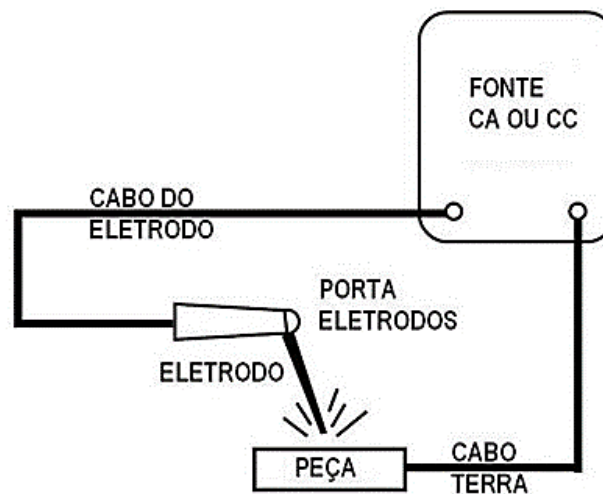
Circuito de soldagem para processo com eletrodo revestido. Fonte: Fortes, 2005.
